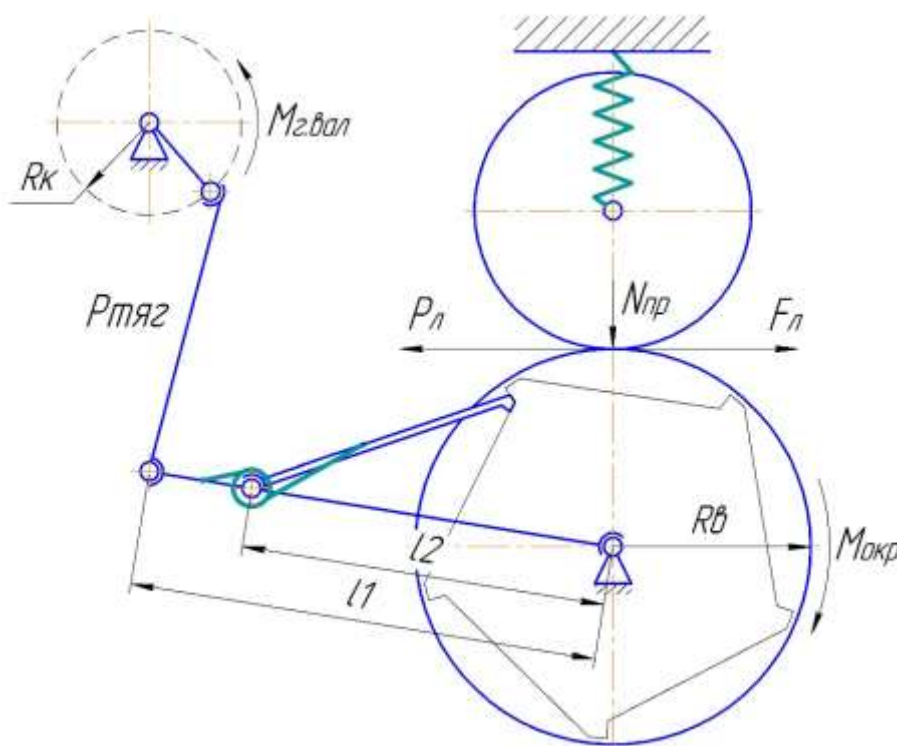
Расчетная схема для определения усилия поджатия ленты валками
